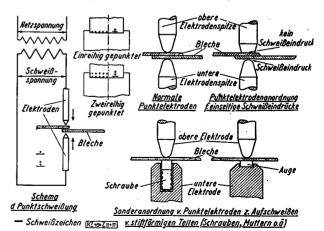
bis 17 Elektrische Punktschweißung
